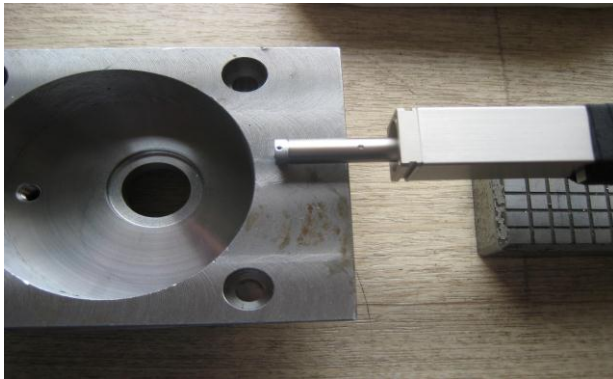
Měření drsnosti povrchu po obrábění na konvenční horizontální frézce
